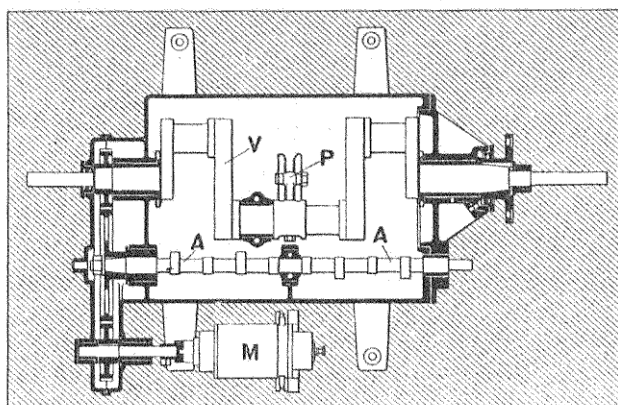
Coupe horizontale d'un monobloc D. F. P.
